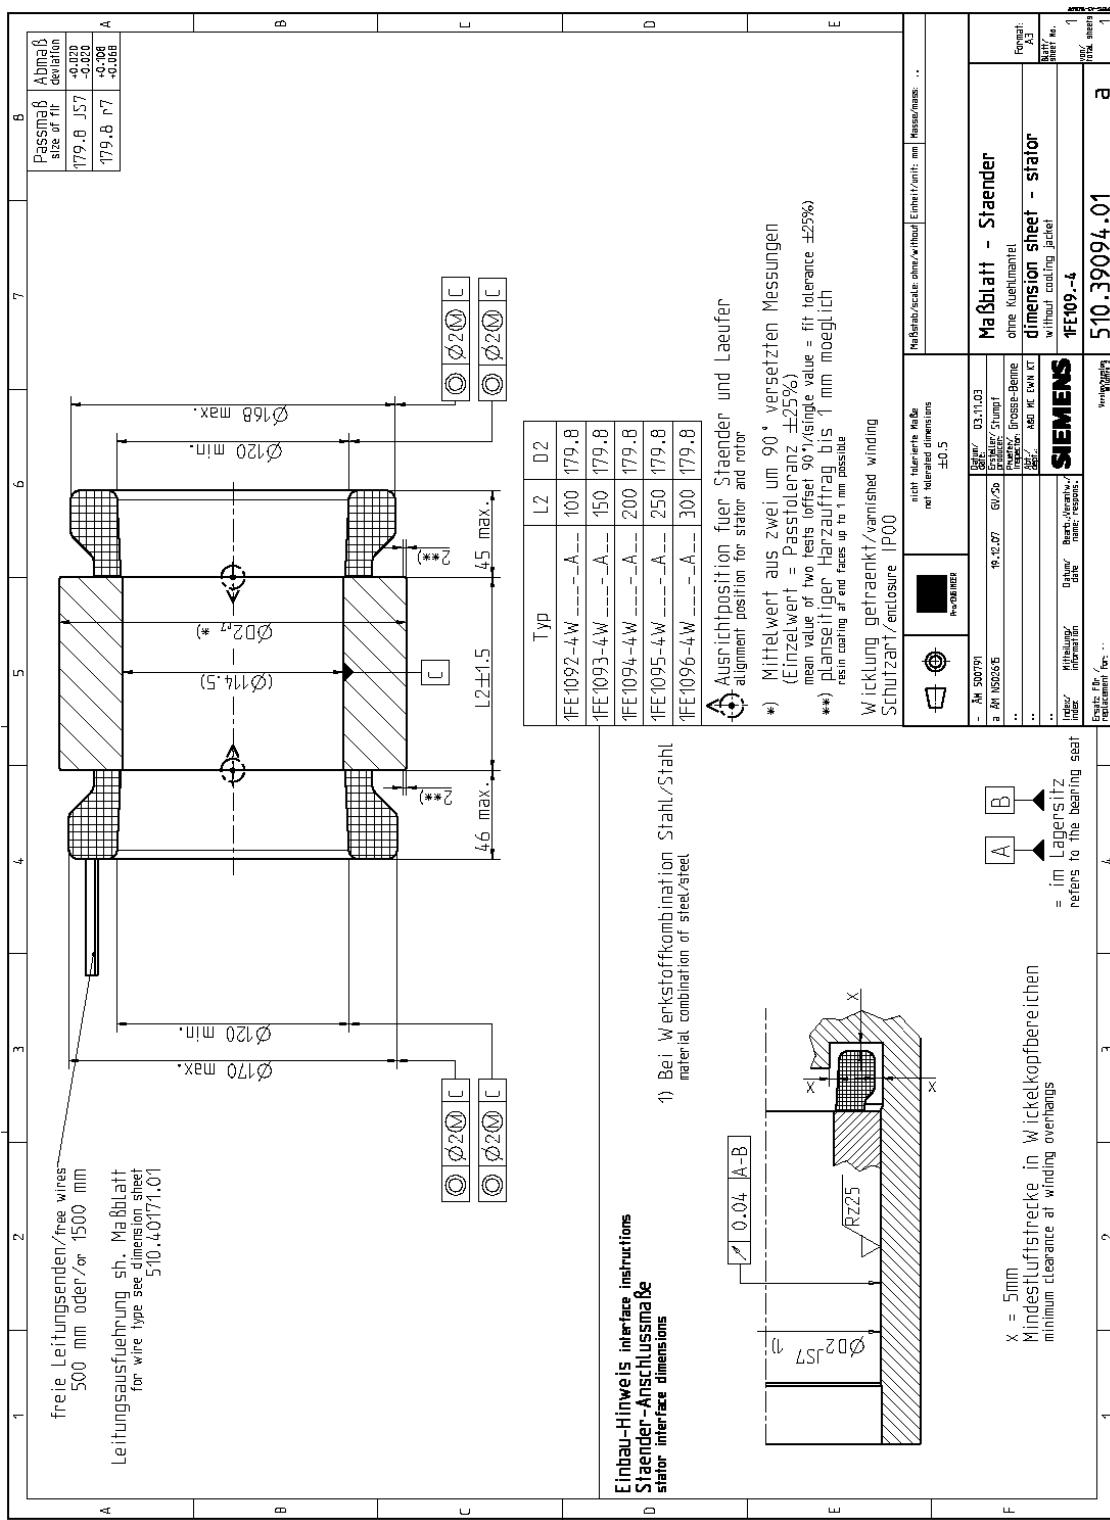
1FE109□-4, Ständer ohne Kühlmantel
